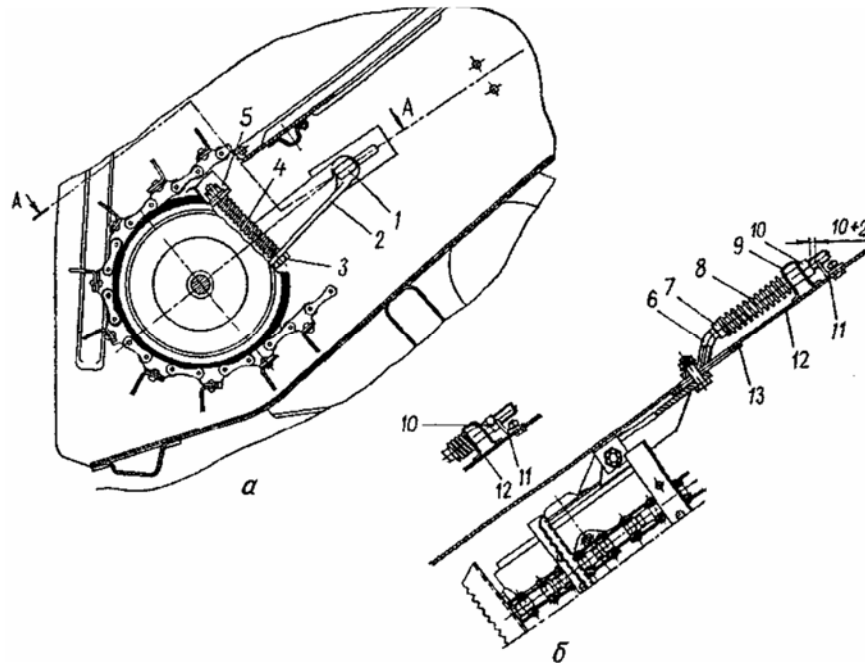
Подвеска ведомого вала транспортера наклонной камеры:
